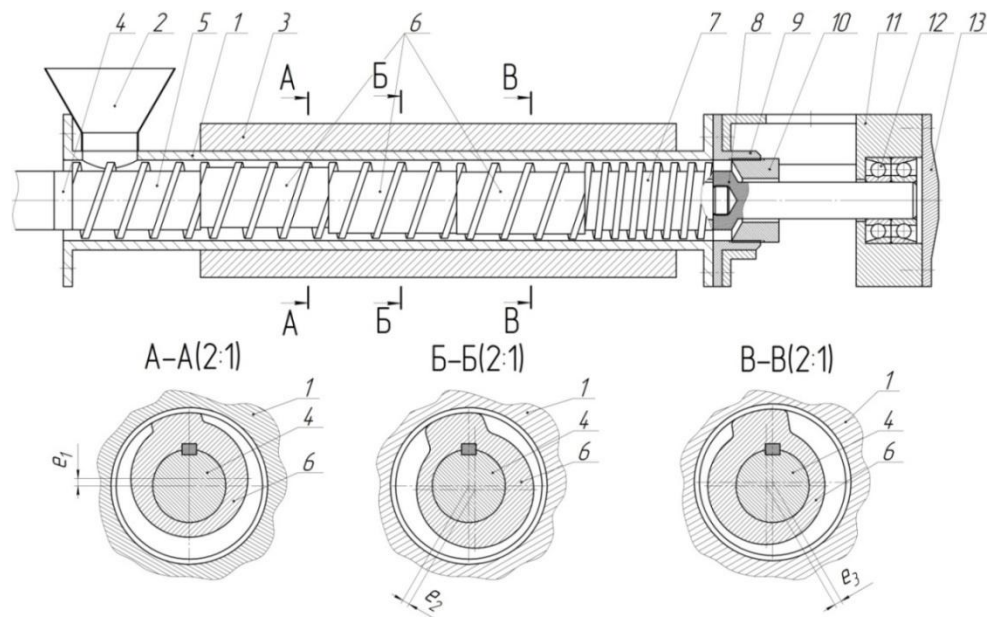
Схема экспериментального экструдера: 1 – корпус; 2 – загрузочная воронка; 3 – температурная камера; 4 – приводной вал; 5 – подающие лопасти; 6 – эксцентриковые лопасти; 7 – прессующие лопасти; 8 – наконечник; 9 – фланец; 10 – гайка; 11 – подшипниковый узел; 12 – подшипник; 13 – крышка; e_1 , e_2 , e_3 – эксцентриситеты нарезки лопастей
